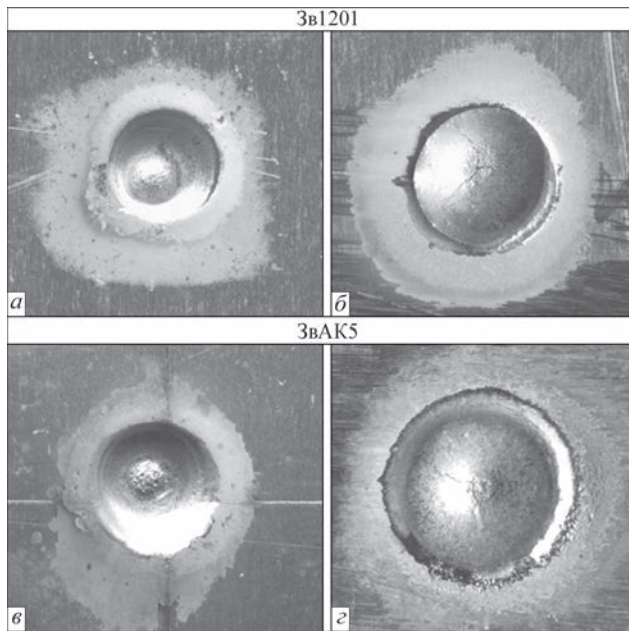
Зовнішній вигляд сплаву Д16Т після виконання технологічної проби «точковий шов» з присадками різного хімічного складу після ручного зварювання (а, б) та після повторного переплавлення (в, г)
